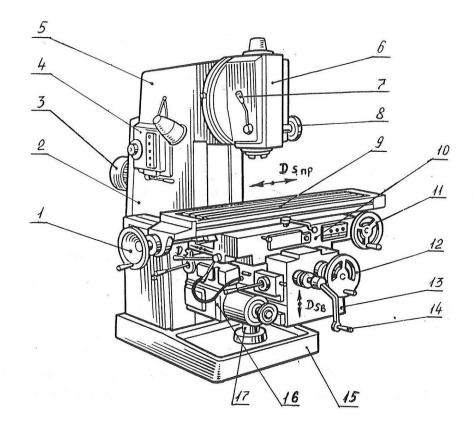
Универсальный вертикально-фрезерный станок:
